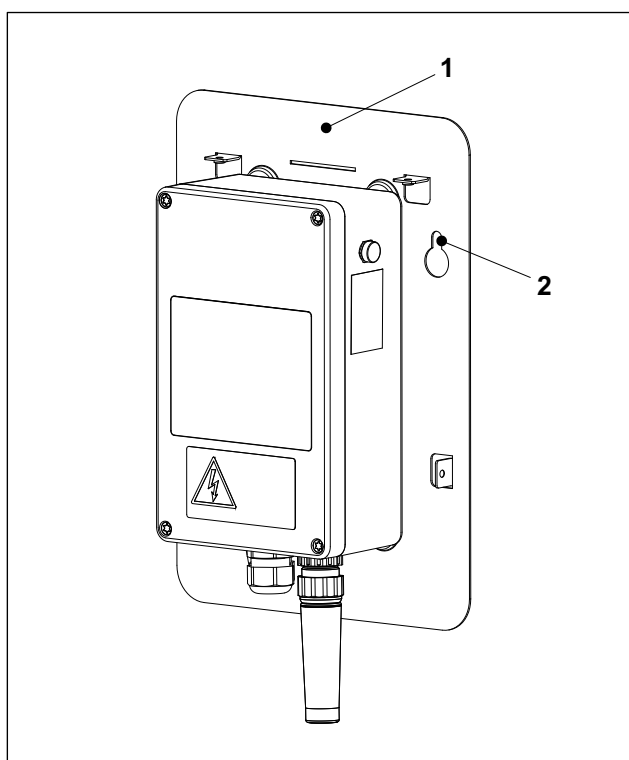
Anschraubplatte mit Elektronikgehäuse
